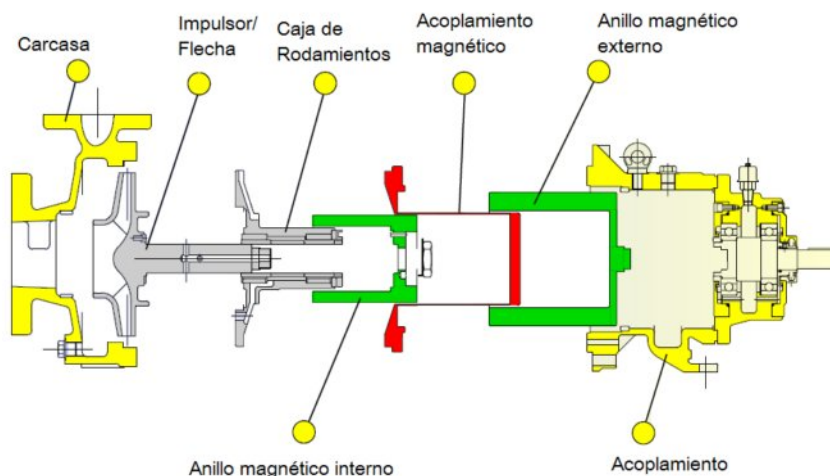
Principales partes dentro del extremo líquido de una bomba magnética centrífuga tipo “seal-less”.
